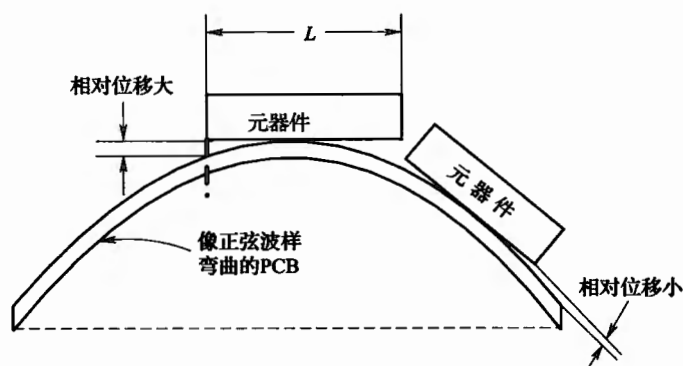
器件装在靠近 PCB 边缘时器件与 PCB 间的相对运动会减少
